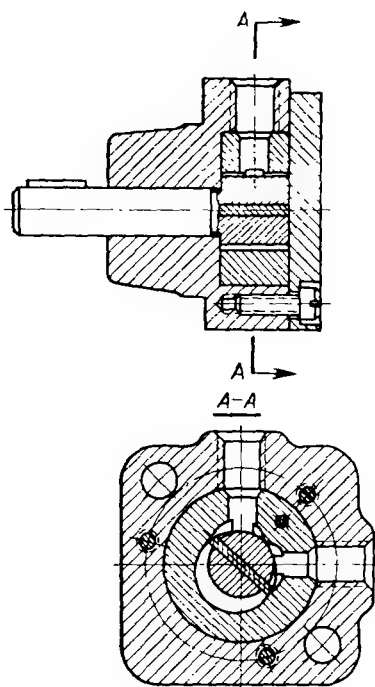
Конструкция пластинчатого насоса типа С12-2 для смазки
